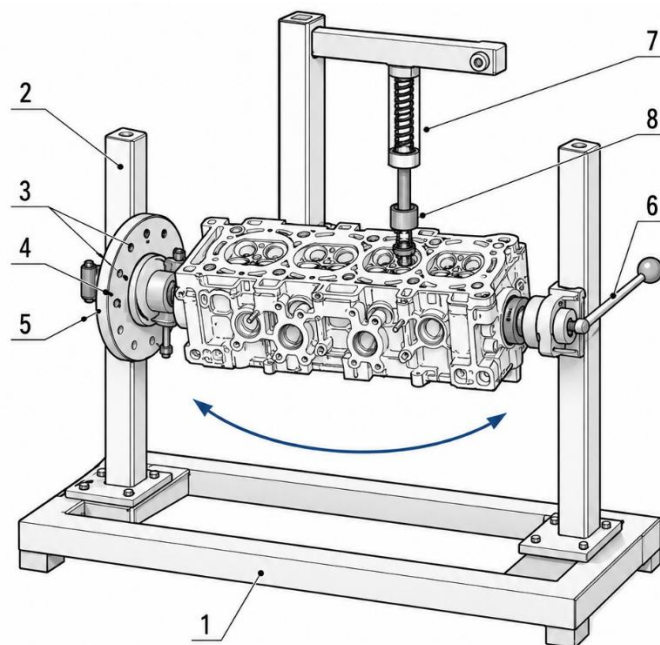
Схема універсального поворотного станда для ремонту головки блока циліндрів:
